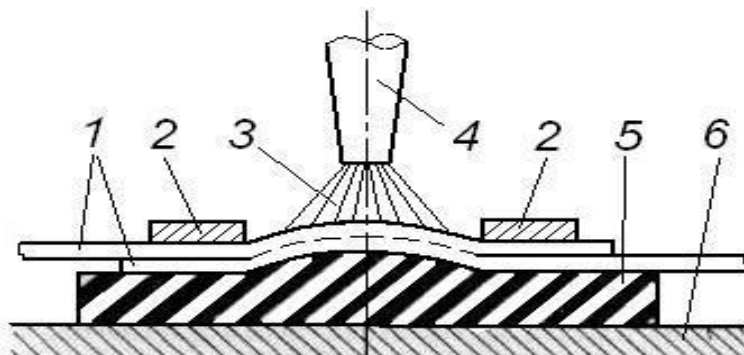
Схема зварювання нагрітим газом плівок: 1-плівки; 2-обмежувачі стрічки; 3-потік газу; 4-наконечник нагрівача; 5-пружна підкладка; 6-жорстка основа.
